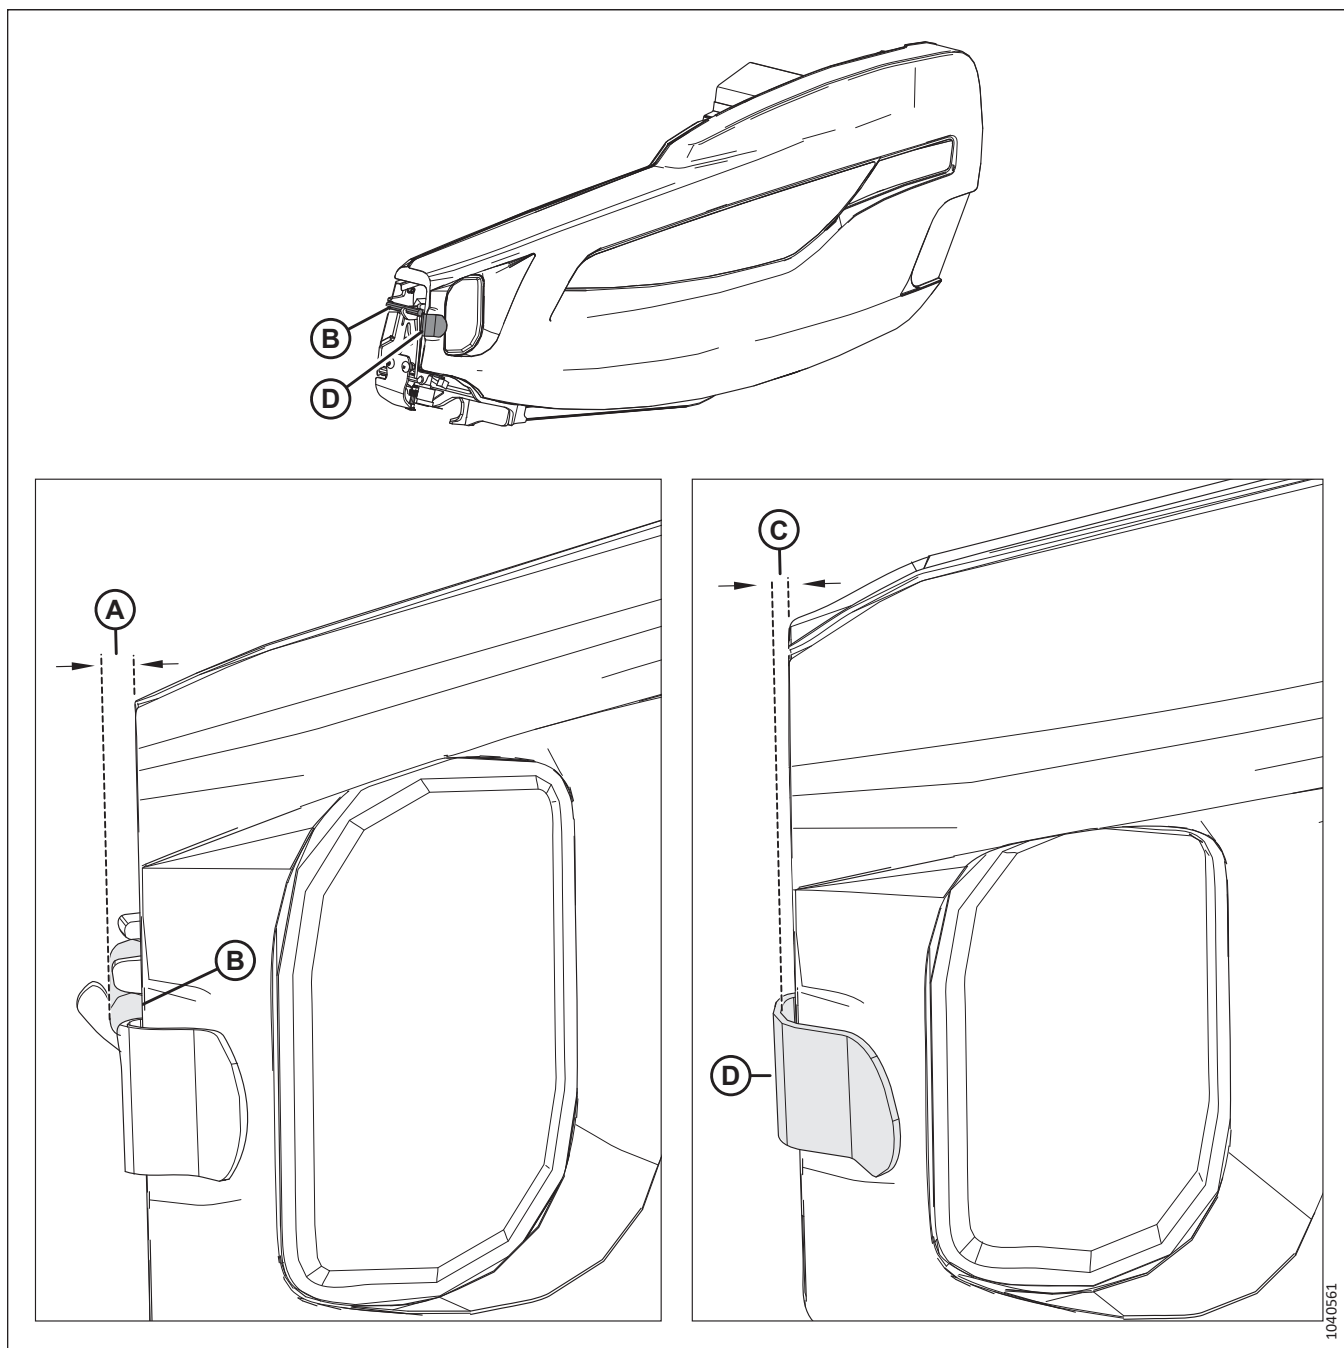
Опорний кронштейн бокового щитка жатки
